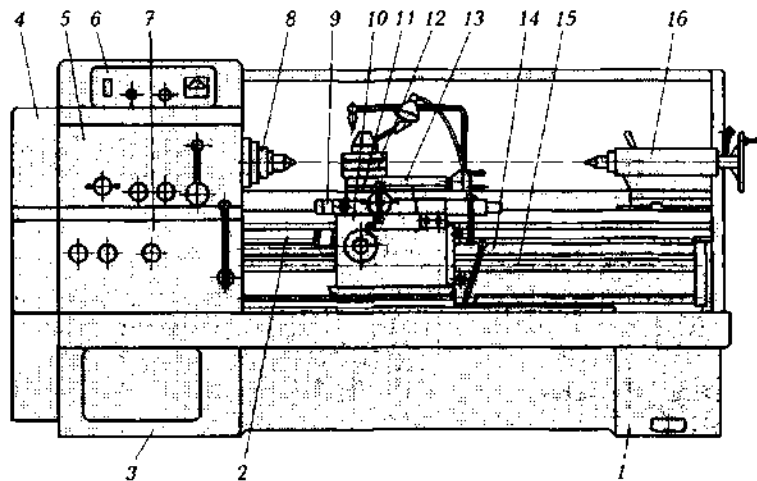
Токарно-винторезный станок модели 16К20:
